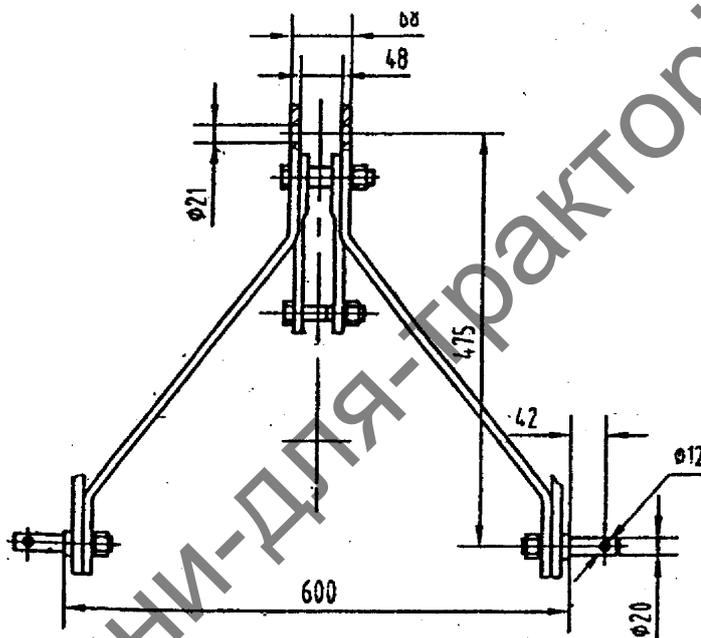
Основные линейные размеры механизма навески почвофрезы.
